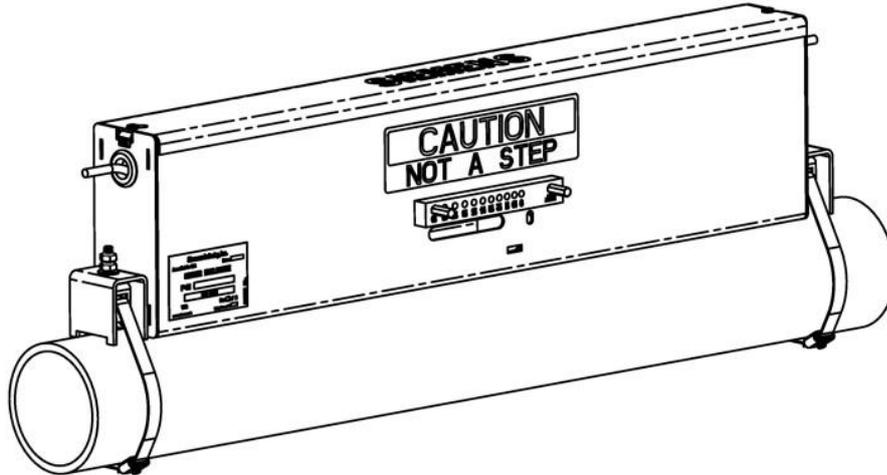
Одинарный корпус с установленным высокоточным датчиком
